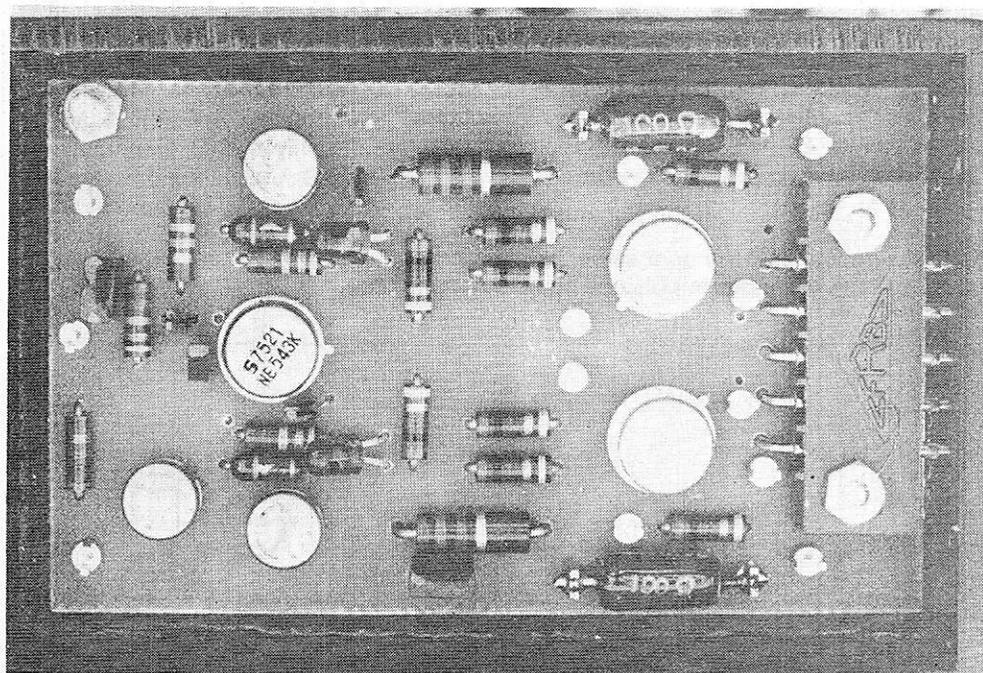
Vue du montage presque terminé, couvercle enlevé. Il manque les fils de liaison aux transistors de puissance.
